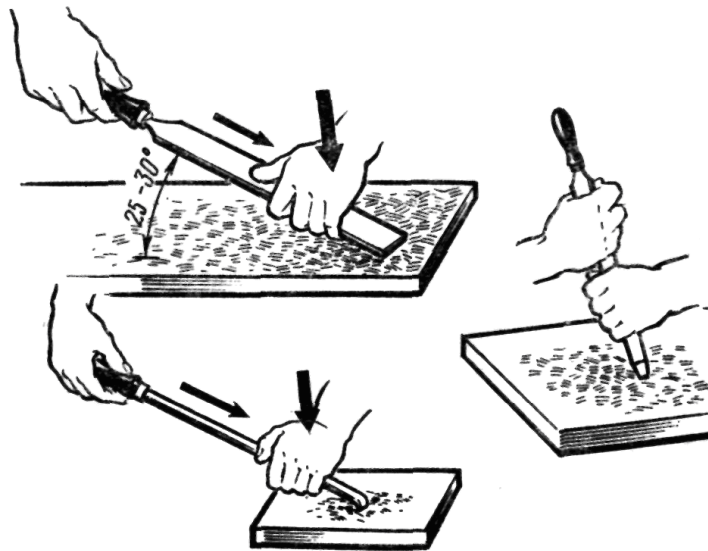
Прийоми шабрування плоскої поверхні.
